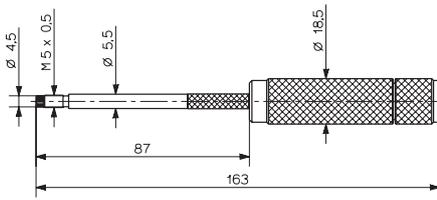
Reibwerkzeug für Bohrung Typ 1300A79
